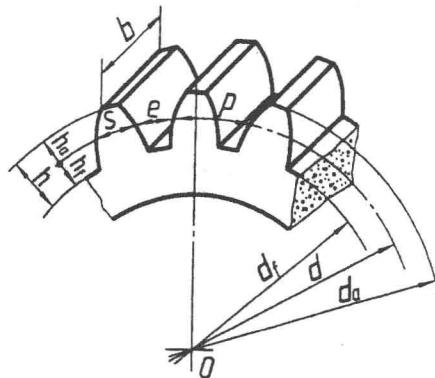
直齿圆柱齿轮各几何要素的名称及代号
